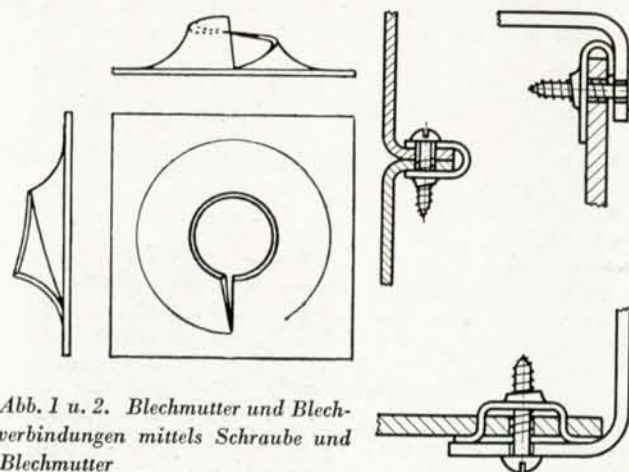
u. 2. Blechmutter und Blechverbindungen mittels Schraube und Blechmutter
